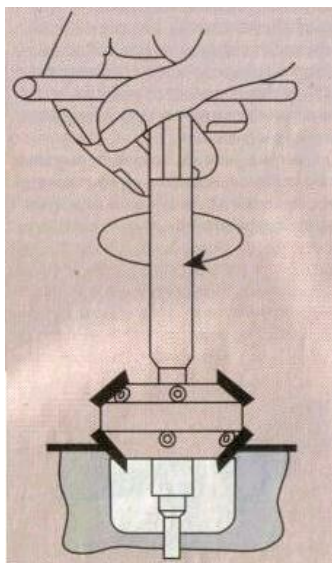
Ручна обробка робочої і головки допоміжна фаски сідла фрезерною головкою.
